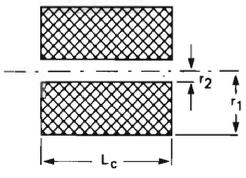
Struttura di principio della bobina di eccitazione di un microinterruttore reed.
